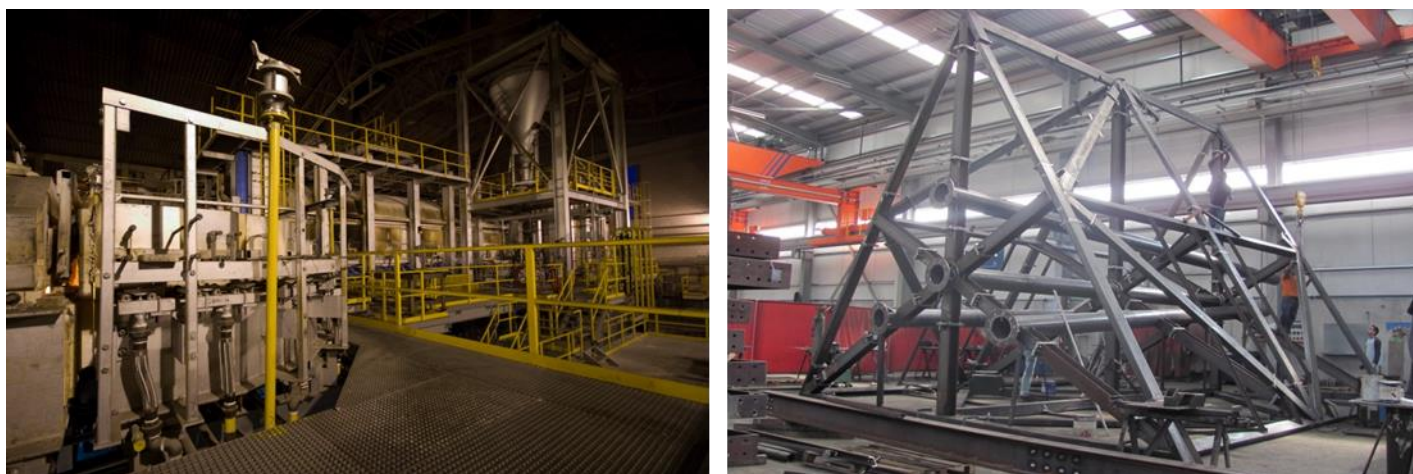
Exemplos de estruturas metálicas fabricadas pela empresa
